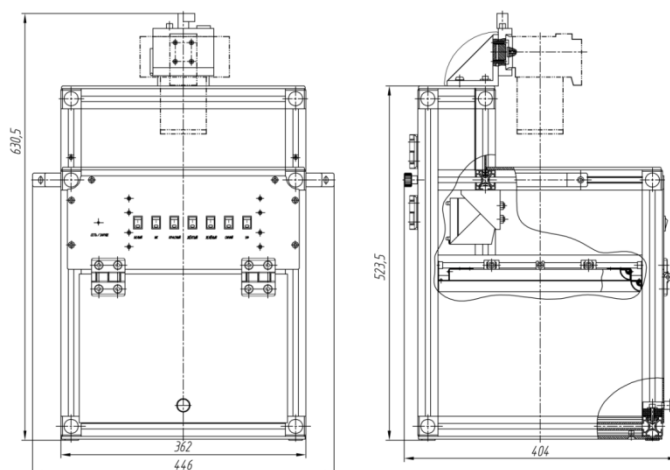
Габаритный чертеж фотобокса (без бленды)
